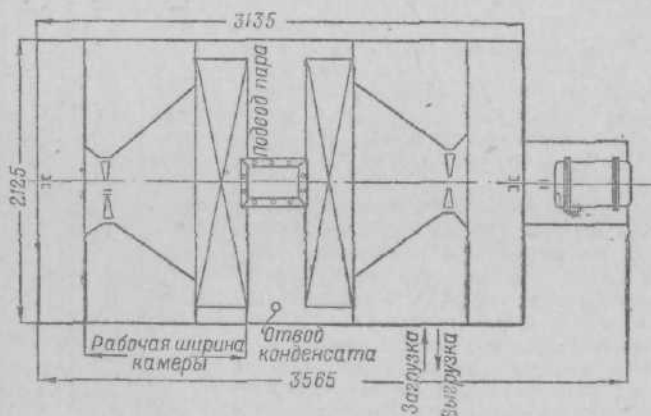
Двухкамерная сушилка КС-2 периодического действия (габаритный чертеж)
